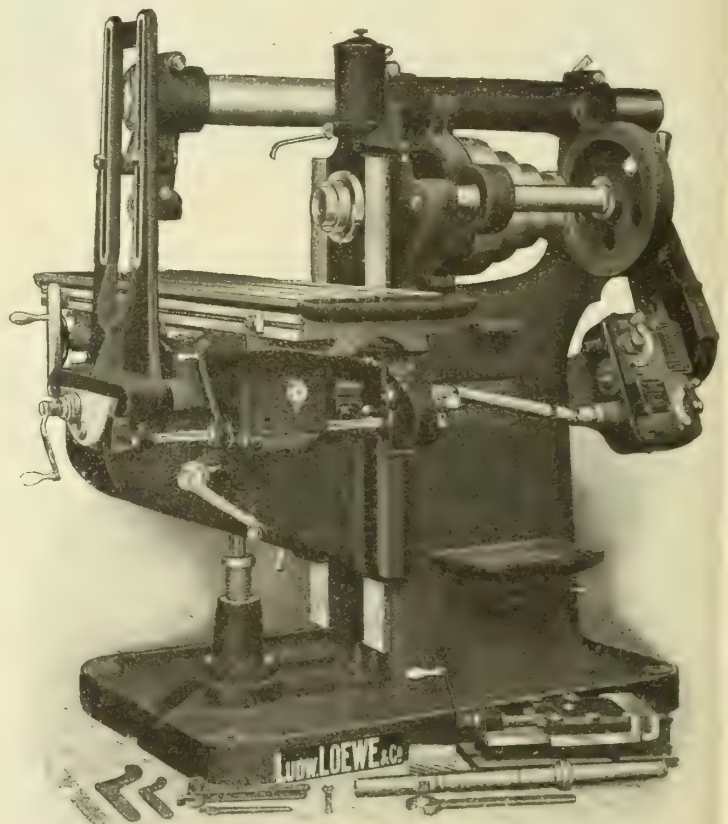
Selbsttätige Fräsmaschine mit fester Arbeitsspindel
